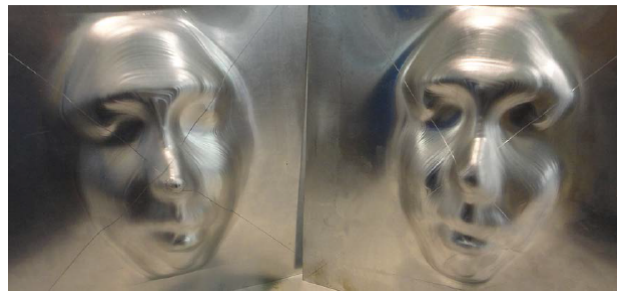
Superfícies de geometria complexa obtidas pelo processo de estampagem incremental [30].
